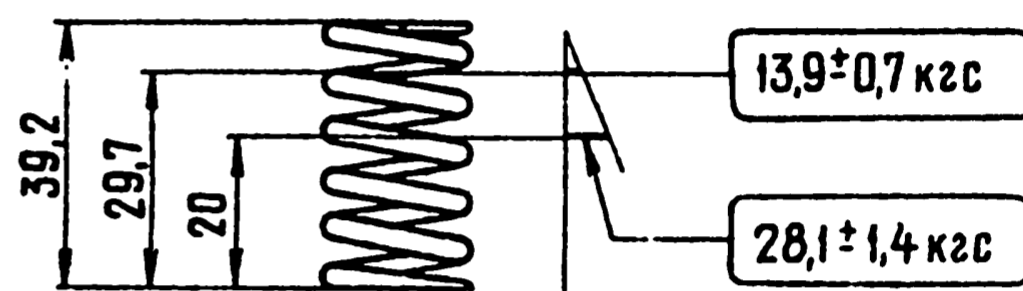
Основные данные для проверки внутренней пружины клапана
